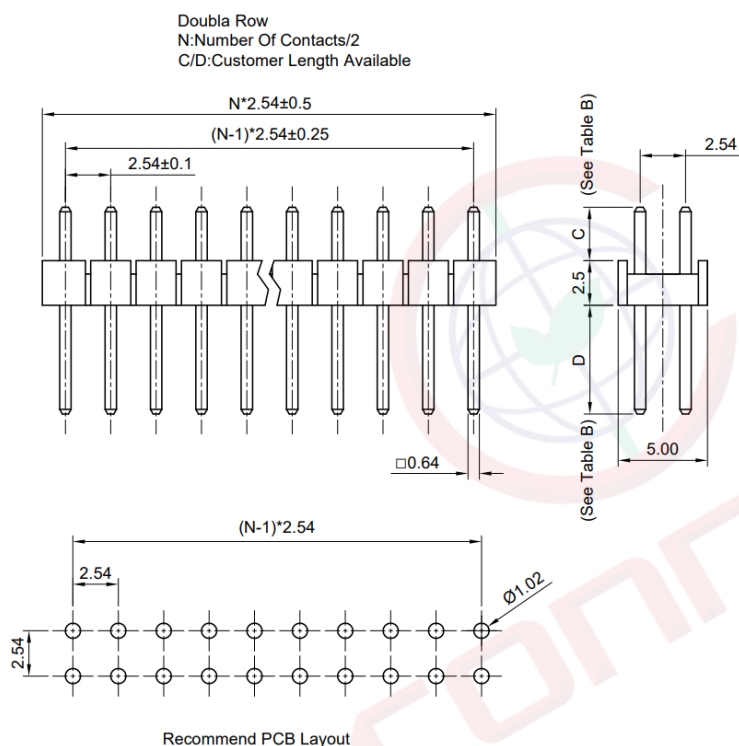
Параметры корпуса соединителя PLD-6
